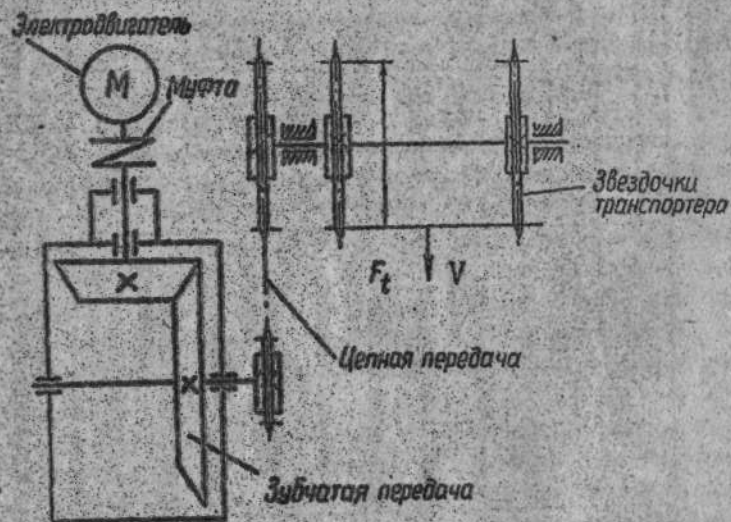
Схема привода цепного транспортера для загрузки багажа в самолет
